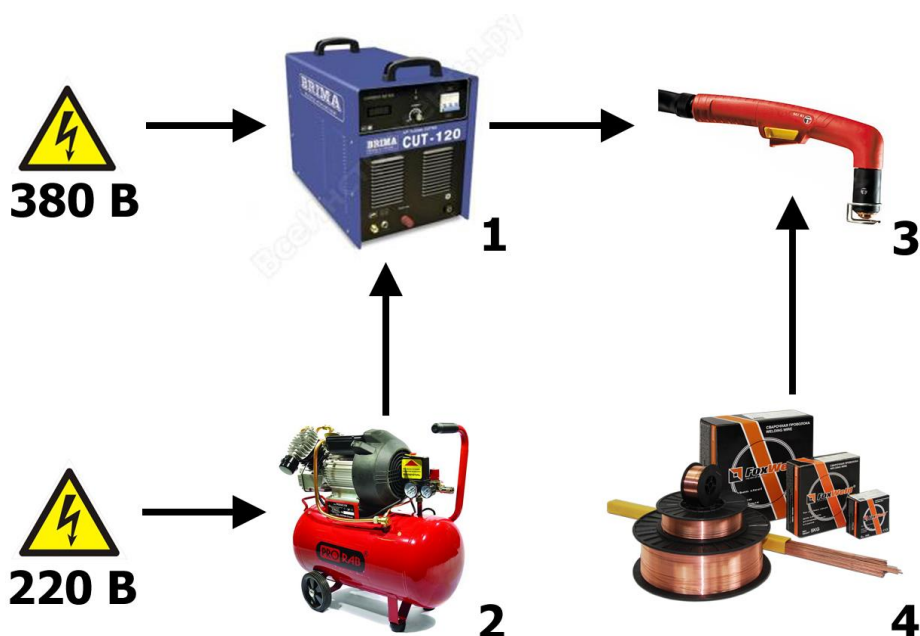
Элементы оборудования для напыления сжатой дугой:
